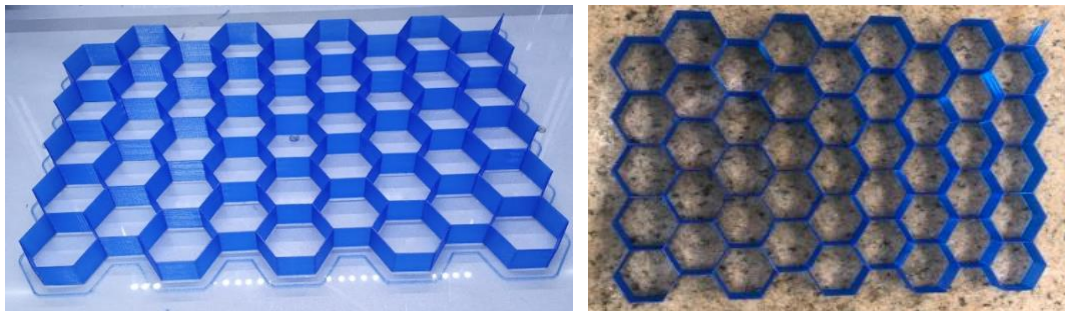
1) Honeycomb em processo de impressão; 2) Honeycomb impresso em material PLA
